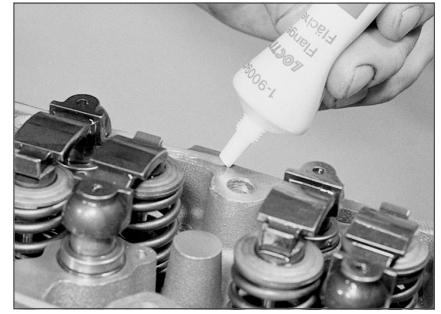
Нанесите слой герметика на стыковочную поверхность головки и установите корпус распредвала
